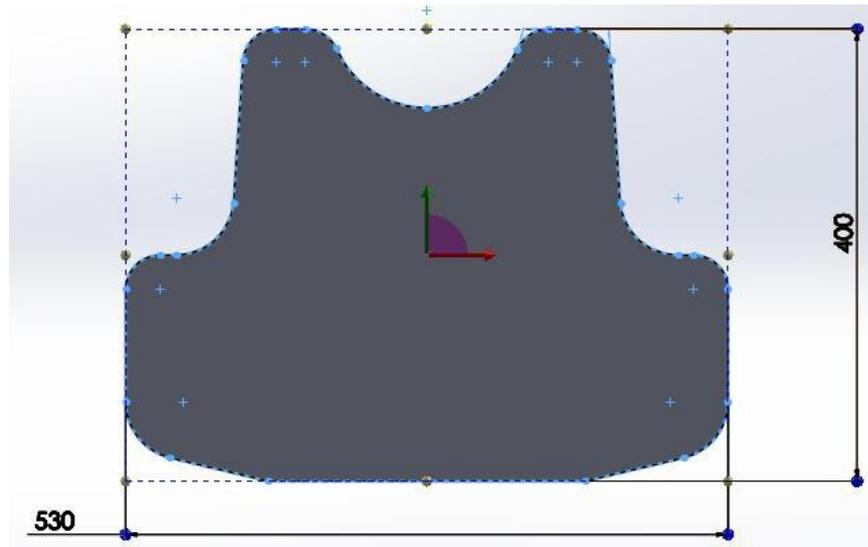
Dimensões gerais do painel balístico flexível (medidas em mm).
